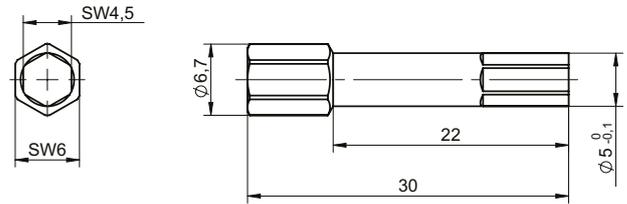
Montagewerkzeug Typ 1300A167 für Screeneinsatz Typ 1193A
